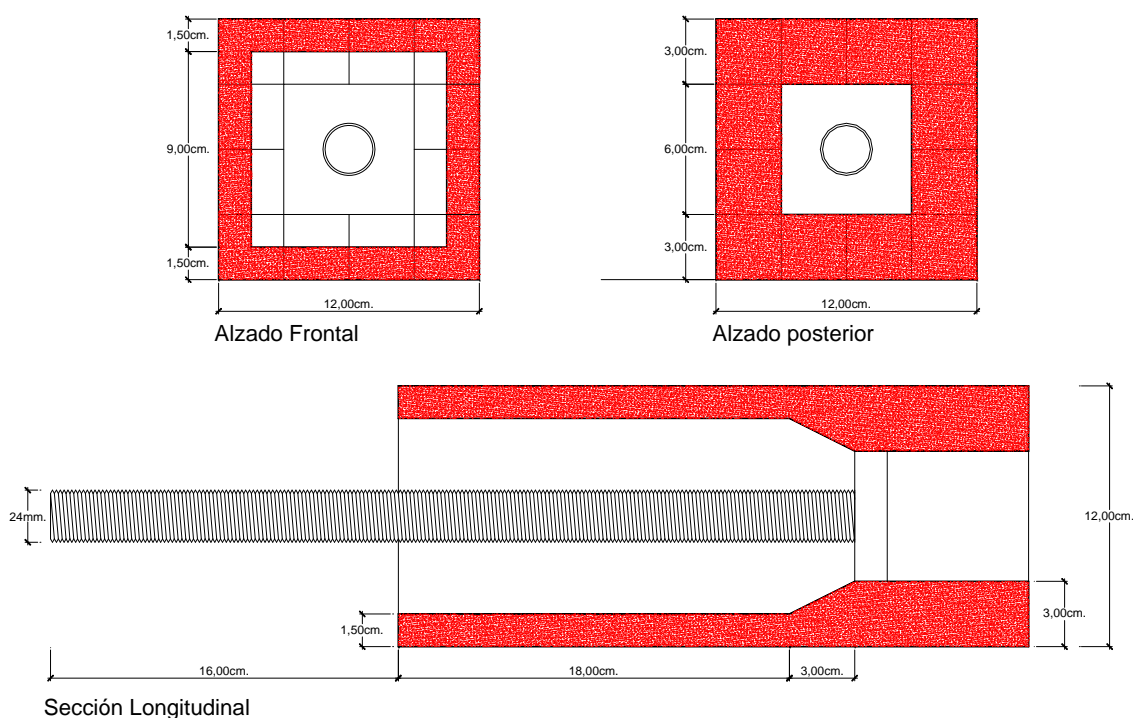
Definición geométrica del enlace extremo de barra a ensayar.
